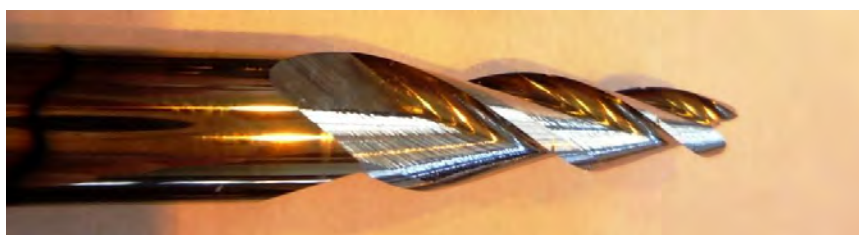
Povlakovaná fréza pro výrobu drobného kolejiva
